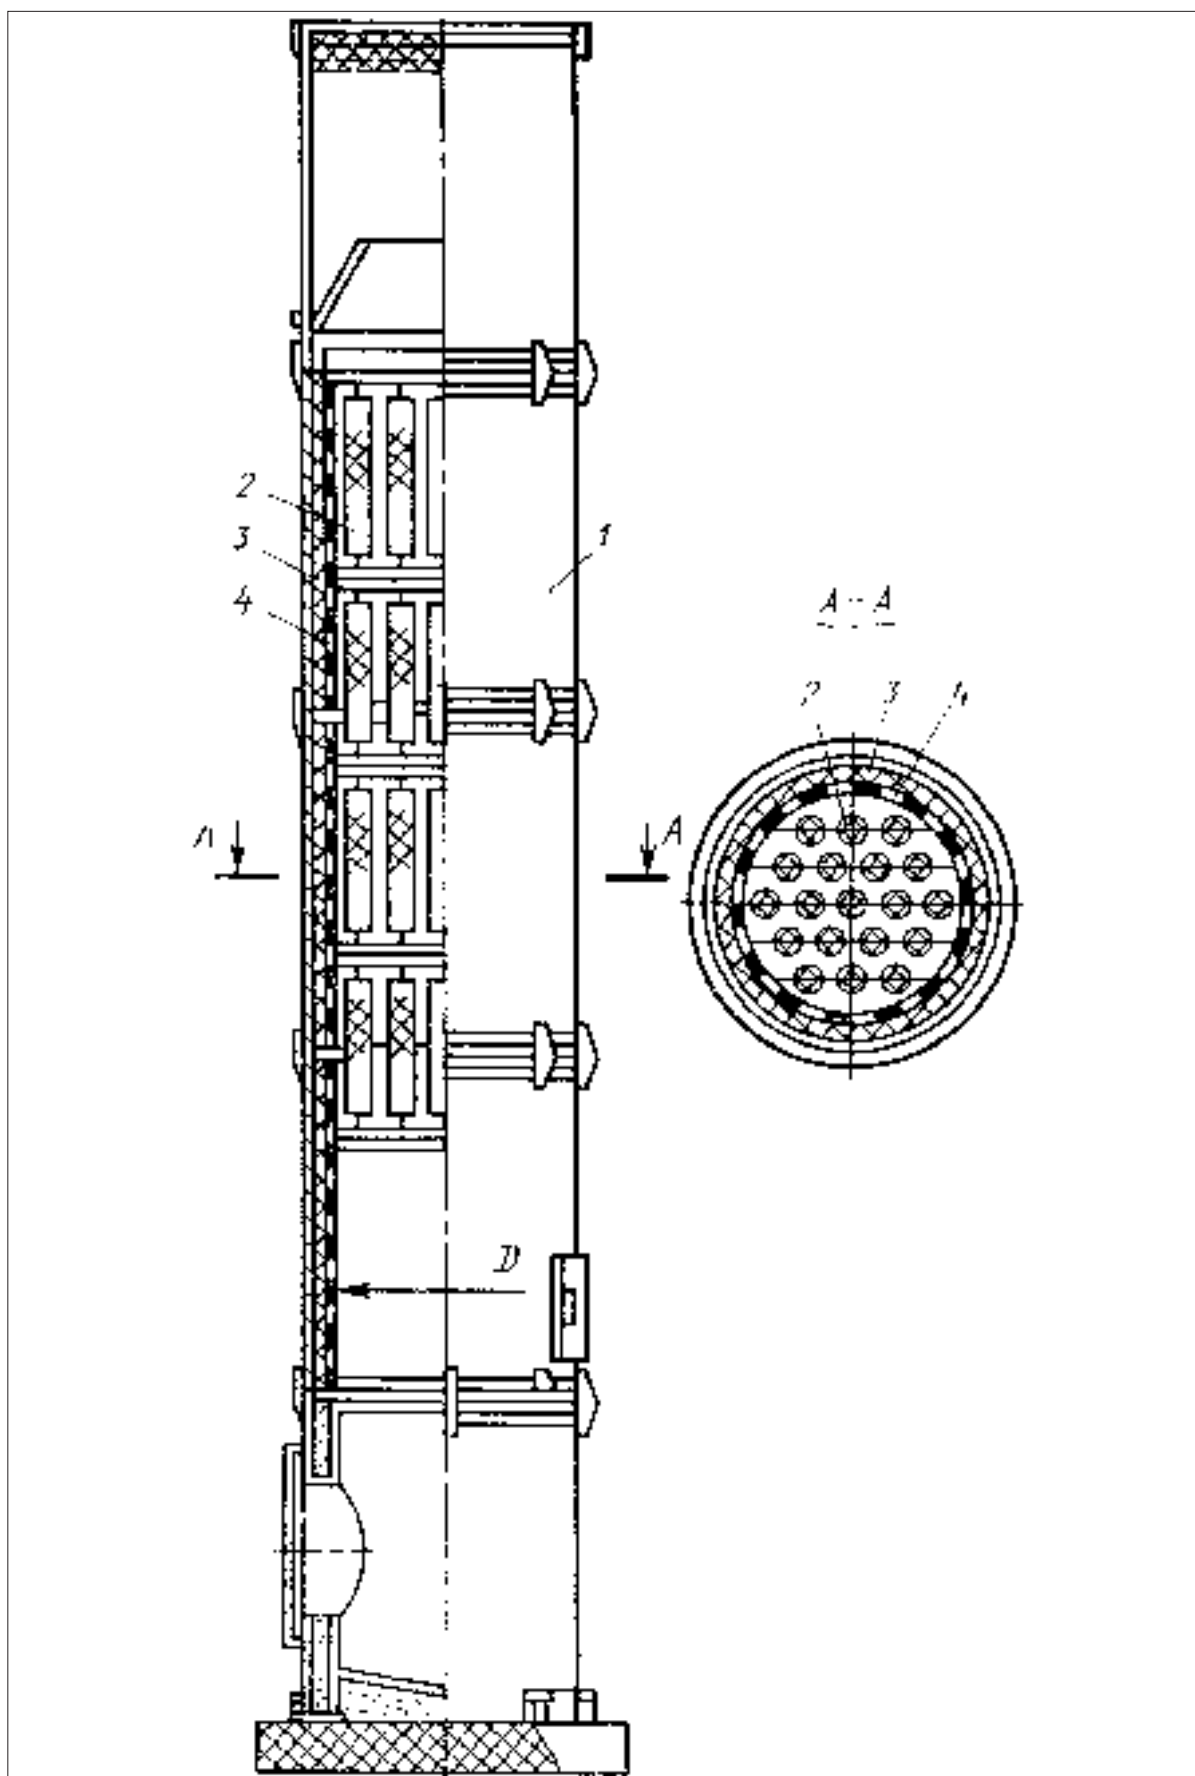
Схема вертикального глушителя шума с цилиндрическими звукопоглотителями:
